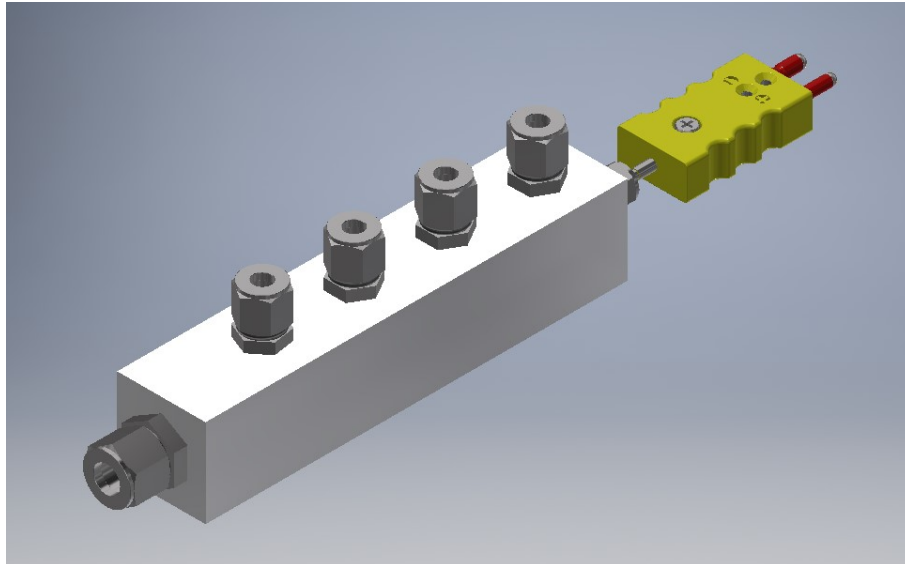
Dibujo CAD representativo de manifold manufacturado.
